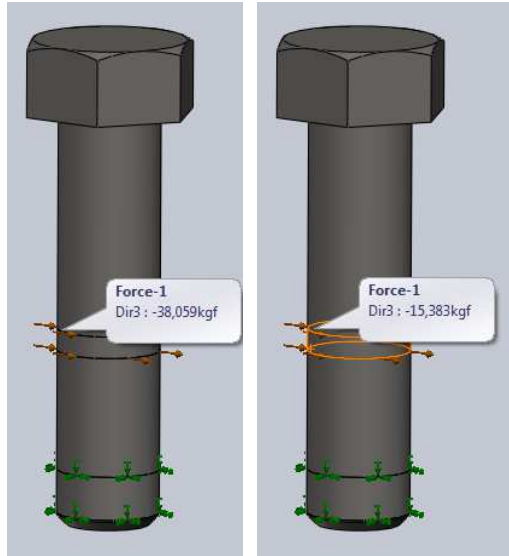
Cargas aplicadas en el eje derecho que soporta al resorte a tracción.
